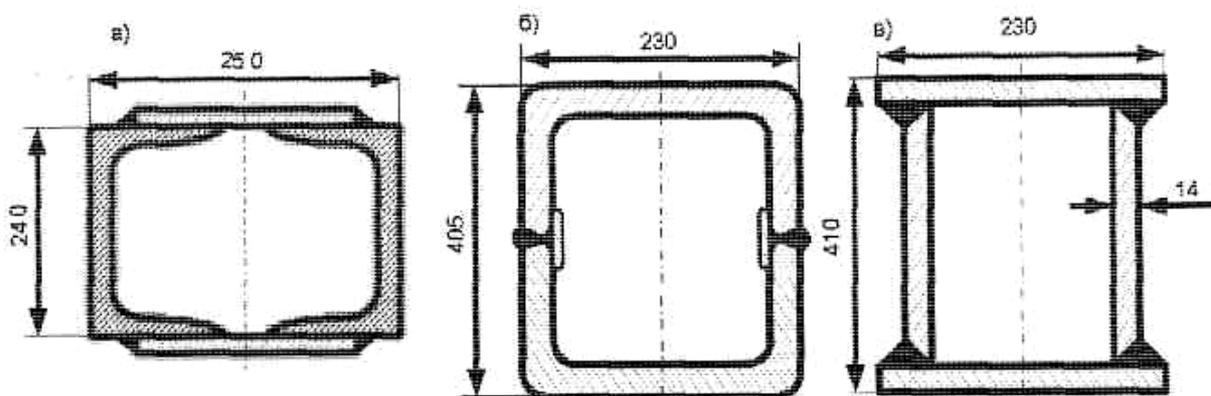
Поперечные сечения продольных балок сварных рам тележек
